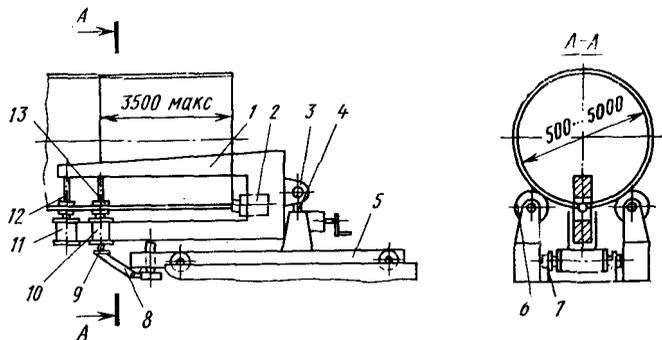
Установка для механизированной сборки кольцевых стыков цилиндрических сосудов
